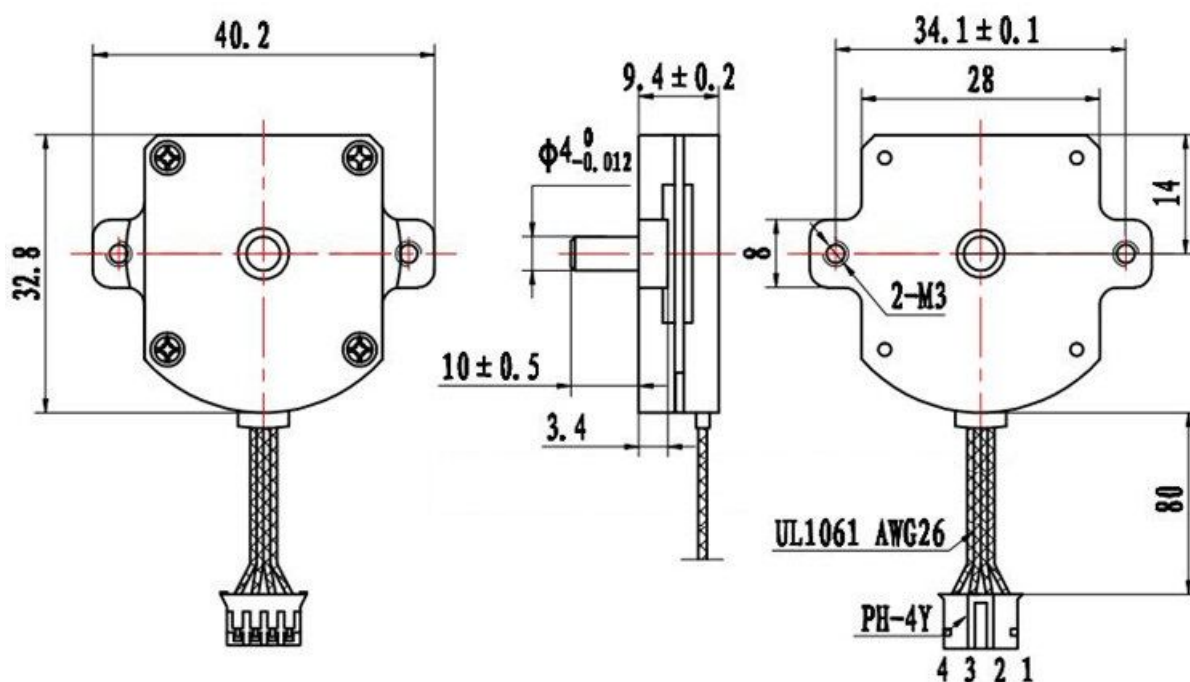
Габаритные размеры шаговых двигателей серии 28BYGH10
